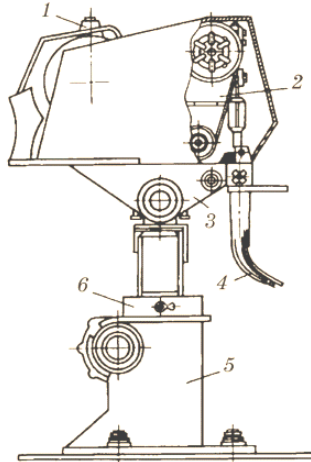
Наплавочна вібродугова головка ОКС 6569:
